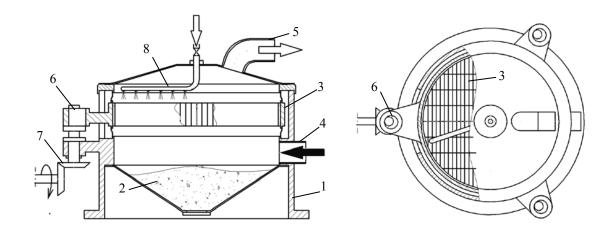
Конструктивная схема пылеочистителя: 1 - корпус; 2 - бункер-пылесборник; 3 - сепарирующая кассета; <math>4, 5 - входной и выходной патрубки; <math>6 - эксцентриковые механизмы; 7 - редуктор привода; 8 - устройство продувки кассеты
